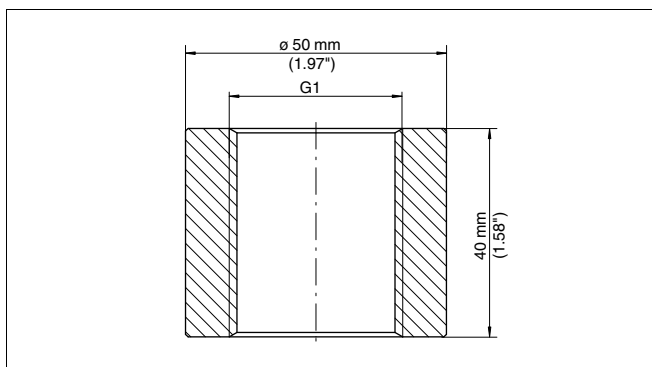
Размеры приварного штуцера - резьба G1 A по DIN ISO 228-1
